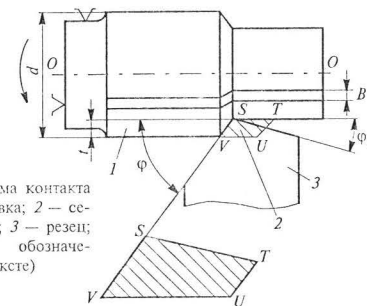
Схема контакта (1 — заготовка; 2 — сечение резца; 3 — резец; (остальные обозначения см. в тексте))
